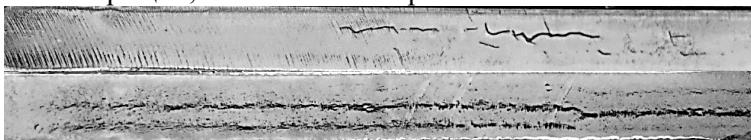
Магнитопорошковые индикации на боковой поверхности пластинчатых образцов
